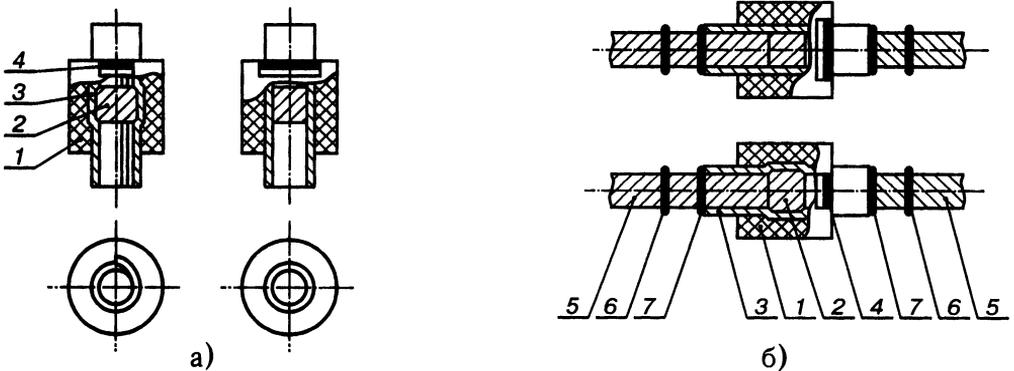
Конструкция термитного патрона (а) и его положение на проводе перед сваркой (б):
